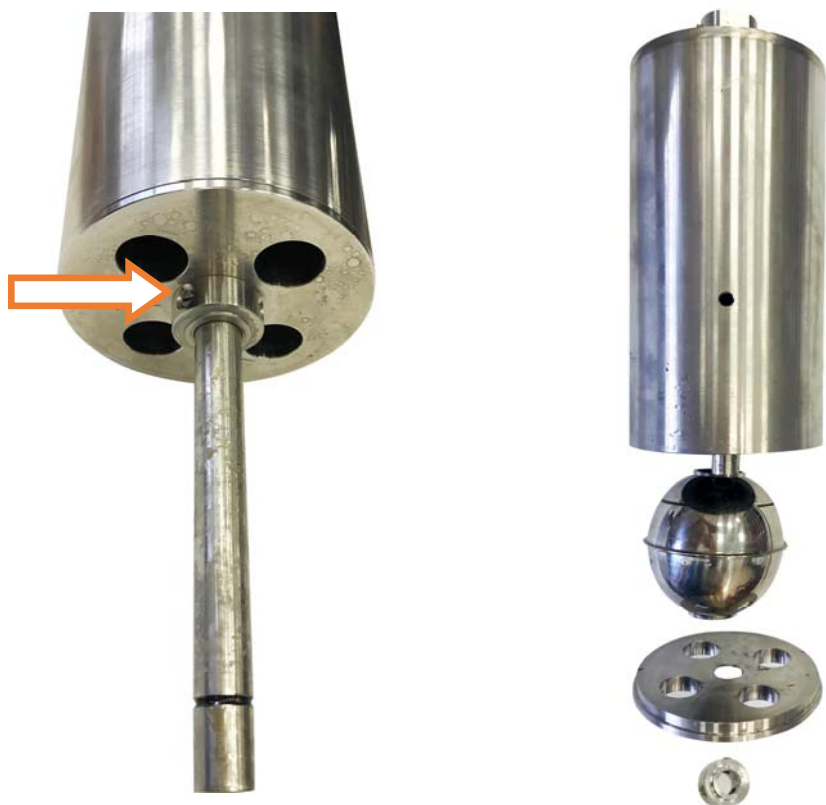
Разбор колокола для установки внутреннего поплавка
